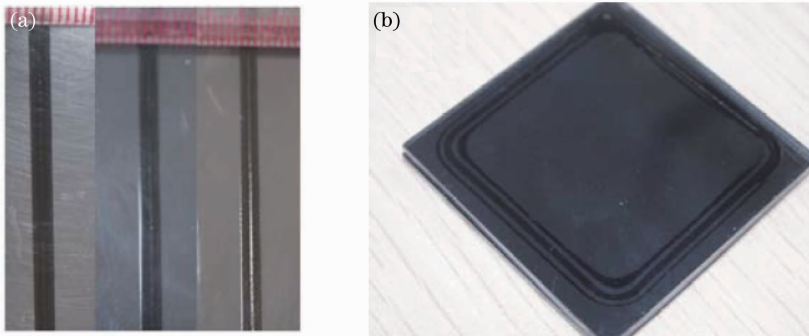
(a) 3 组焊接质量较好的焊缝; (b) PMMA 环焊
